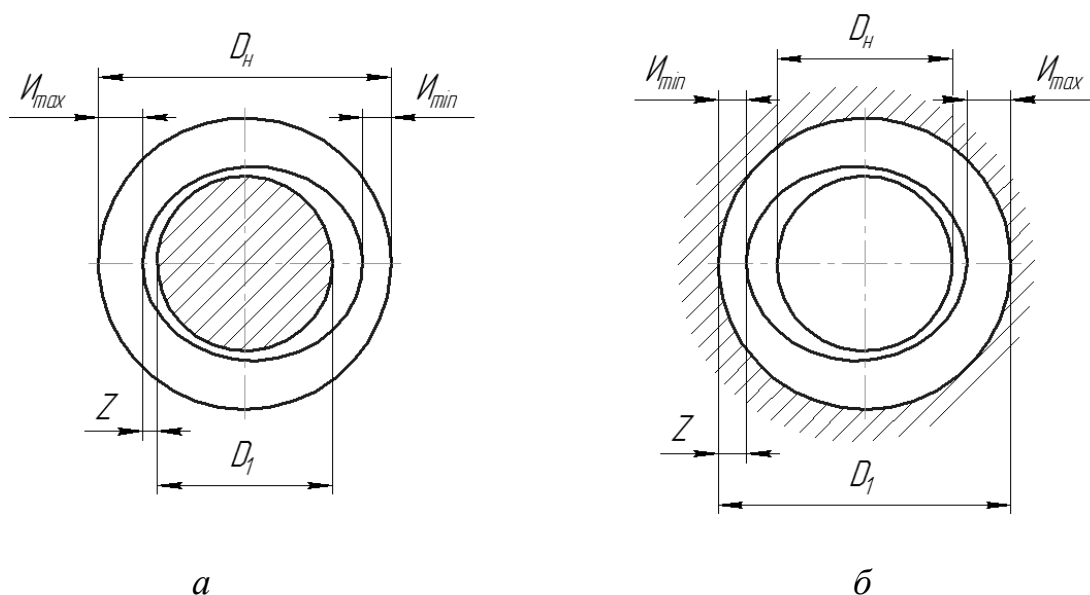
Схема к расчету ремонтных размеров: a – для вала; b – для отверстия
